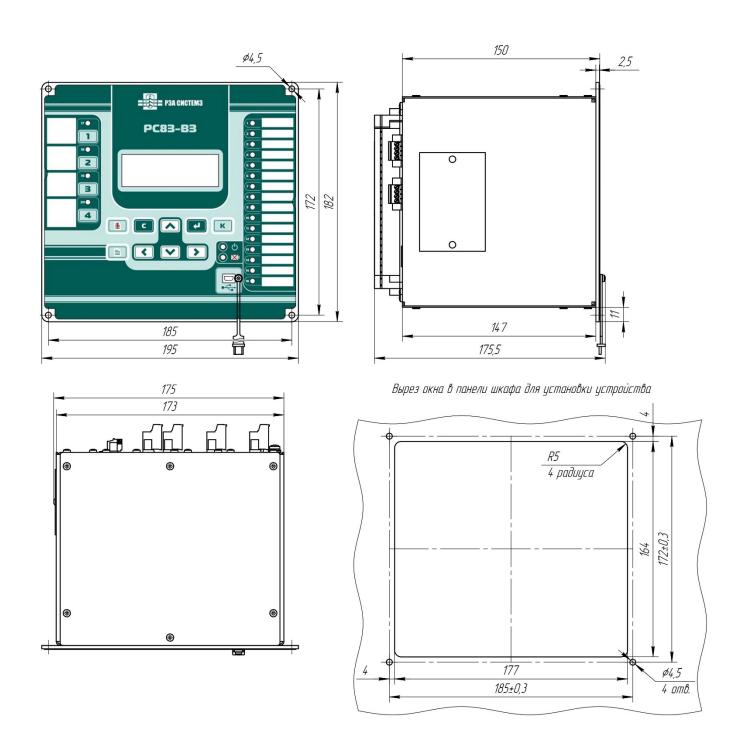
Габаритные и присоединительные размеры устройства РС83-В3
